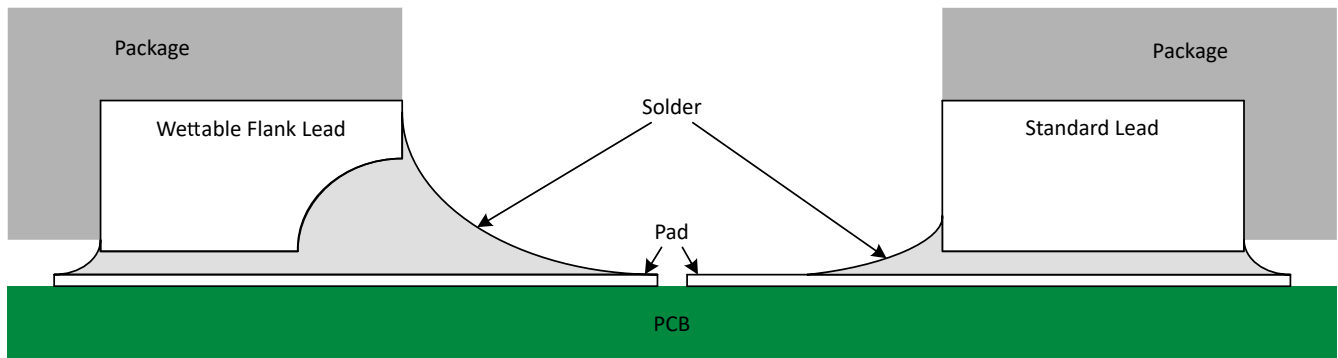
焊接后具有可润湿侧翼的 QFN 封装和标准 QFN 封装的简化剖面图
